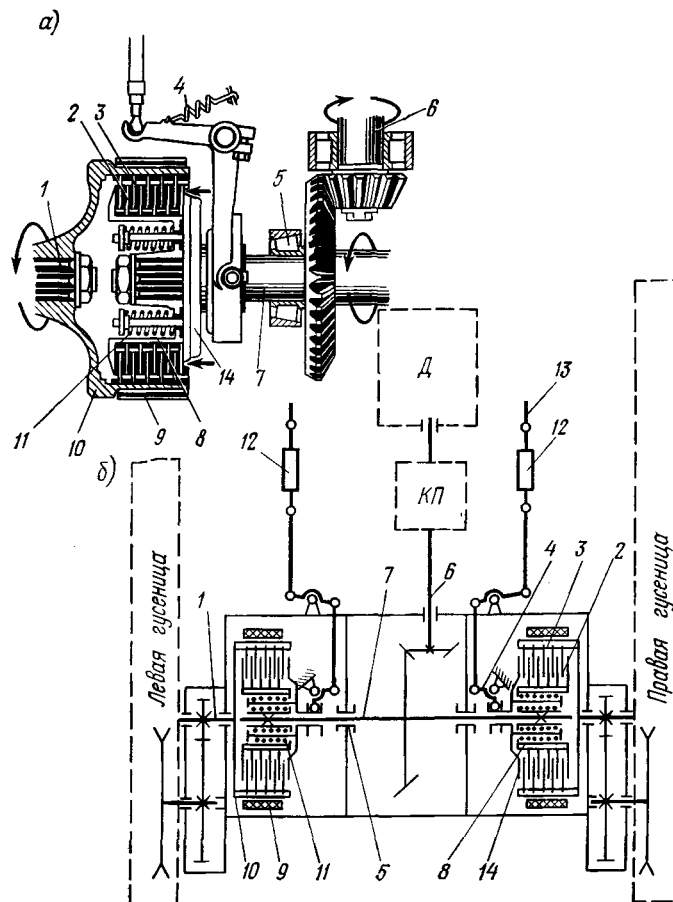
Схема управления движением гусеничной машины с помощью рулевых муфт: а – устройство; б – общая схема передач движения; Д – двигатель; КП – коробка передач
